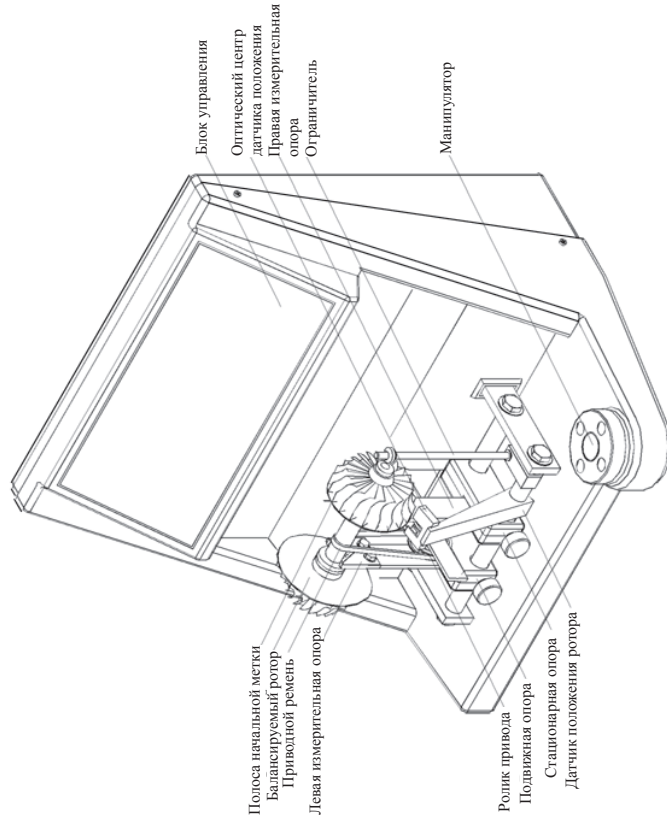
Внешний вид станка «Неотрон СБРТ-1500» и основные узлы
